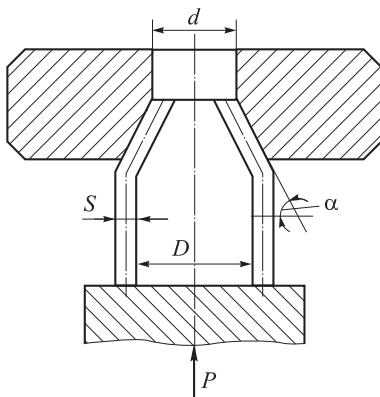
Схема обжига трубчатых заготовок в конической матрице
